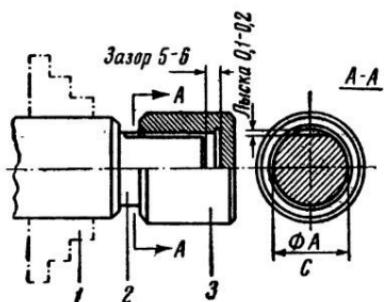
Патронная оправка с лыской для глухих отверстий: 1 — кулачки патрона; 2 — оправка; 3 — обрабатываемая деталь.
